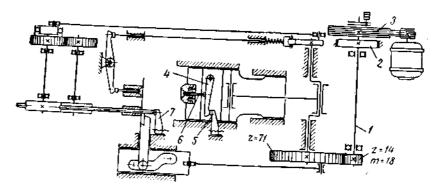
Кинематическая схема холодновысадочного прессаавтомата модели АБ148 для штамповки шариков
